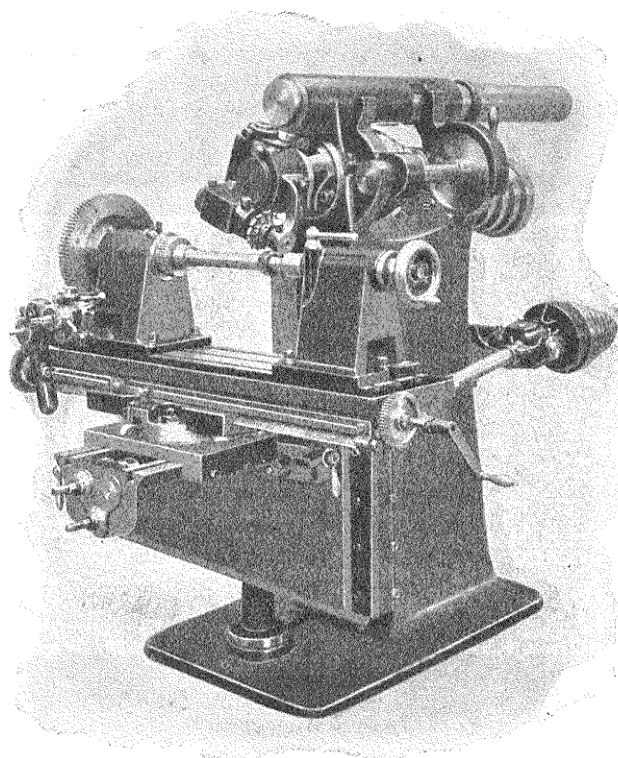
Machine à fraiser universelle Reinecker avec dispositif pour tailler les vis.
